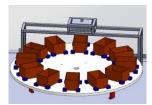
Dimensi Mesin Pengisi Larutan Asam Sulfat Tampak Depan
